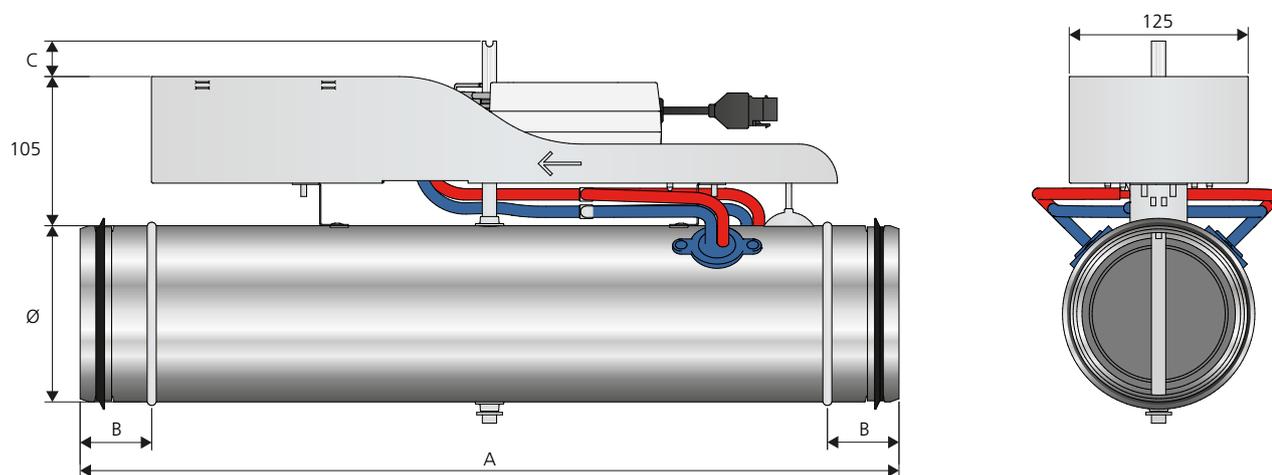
Abmessungen, WISE Damper rund und WISE Damper rund mit Federrücklauf.
